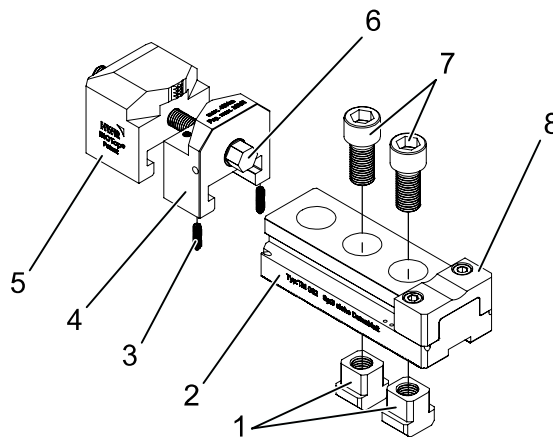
Montaggio delle ganasce di serraggio - mandrino di serraggio grande
